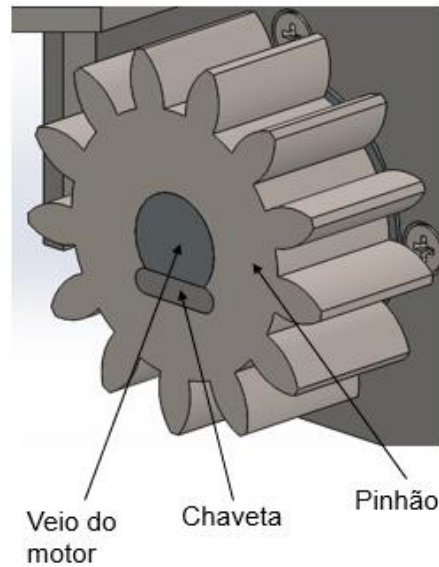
Elementos do conjunto do motor elétrico com o pinhão
